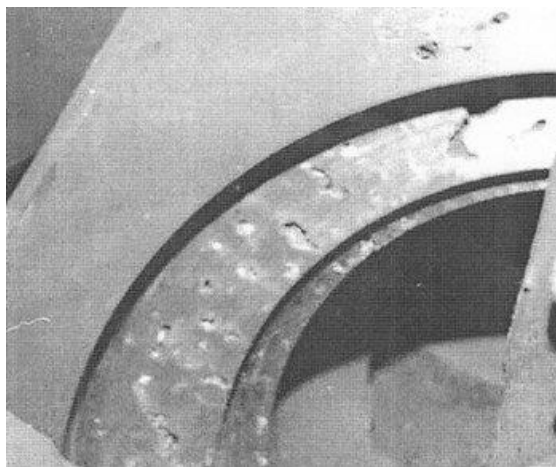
Отливка «Корпус» с газовыми раковинами
